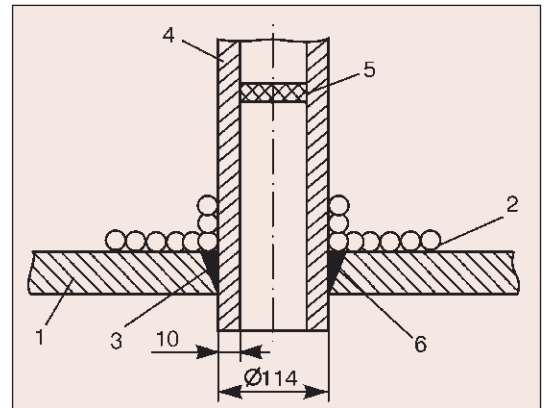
Схема установки электронагревателей КЭН-3 при местной термообработке сварных соединений штуцера размером 114×10 мм: 1 — оболочка шарового резервуара; 2 — витки электронагревателя КЭН-3; 3 — термоэлектрический преобразователь; 4 — штуцер; 5 — теплоизоляционная заглушка во внутренней полости штуцера; 6 — сварное соединение штуцера с оболочкой
